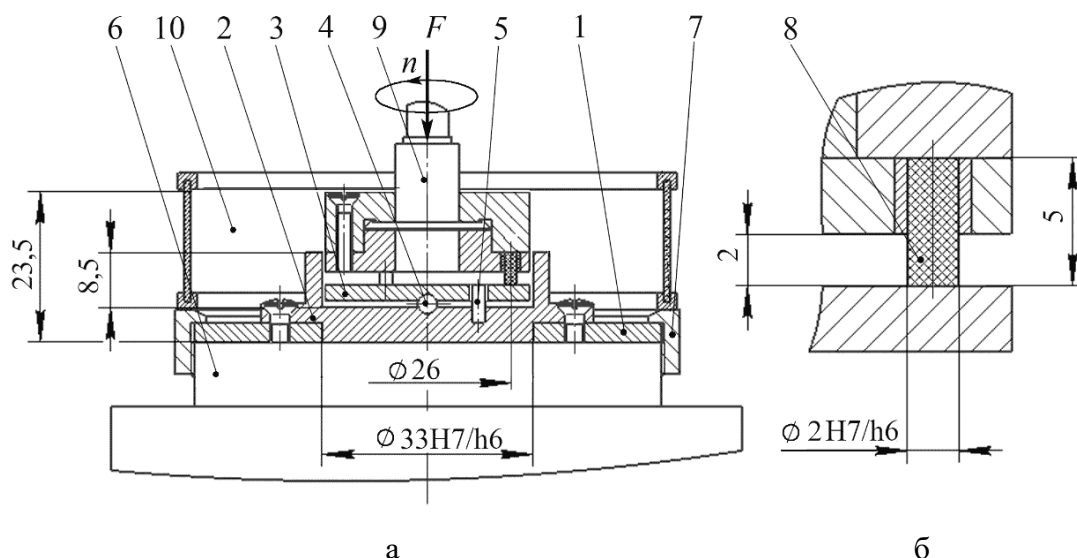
Конструкция трибометрической приставки (а) и метод фиксации образцов в гнездах ротора (б): 1 – диск монтажный; 2 – стакан; 3 – контртело; 4 – опорный шар; 5 – штифт; 6 – обогреваемый столик реометра; 7 – гайка накидная; 8 – образец; 9 – ротор; 10 – защитный экран
